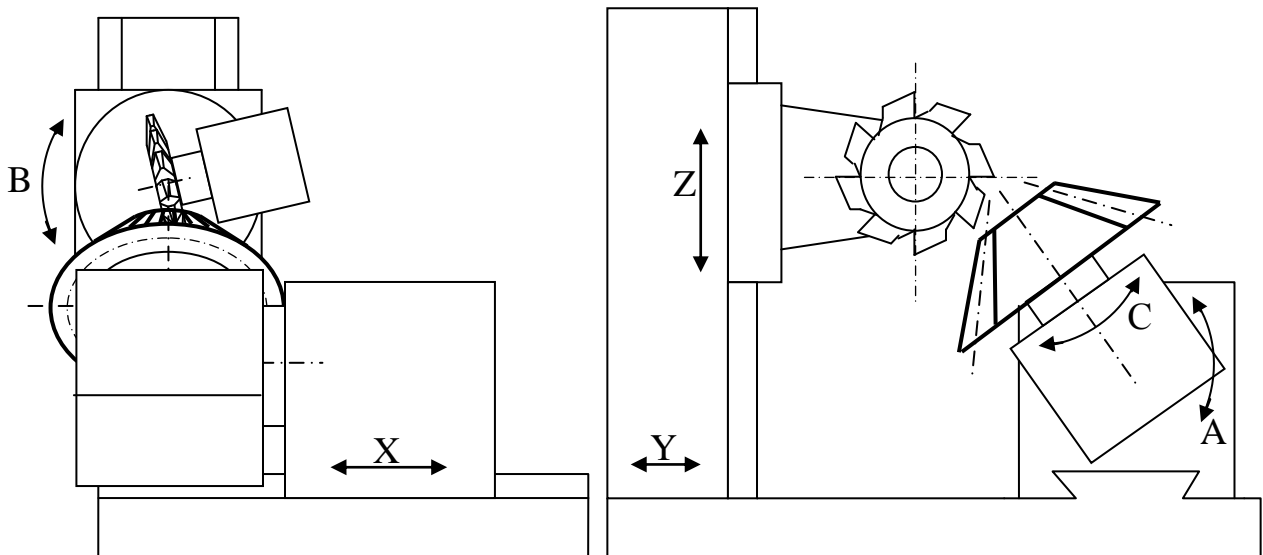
Вариант компоновки универсального зуборезного станка.
